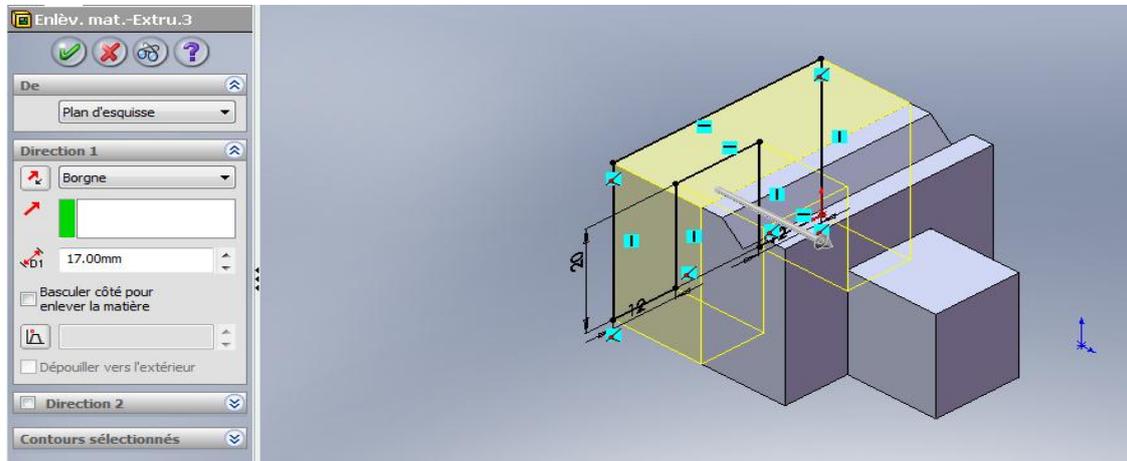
54. Enlèvement de matière sur le plan gauche.
